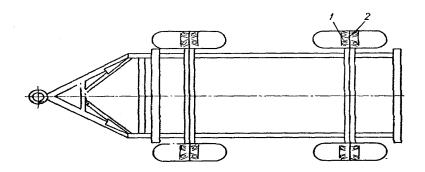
Схема расположения подшипников: 1 — подшипник внутренний; 2 — подшипник наружный
